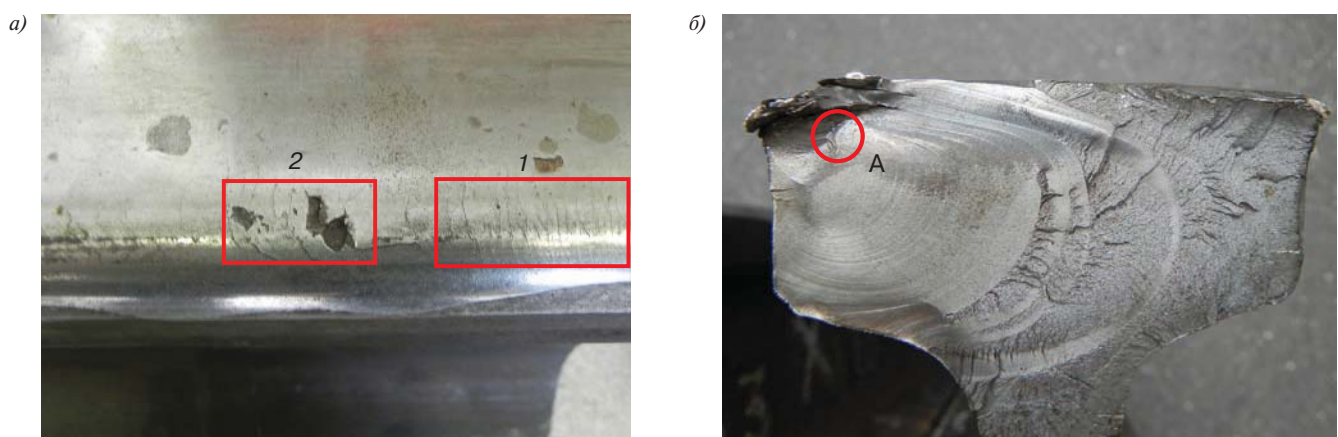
Варианты разрушения в области сварных стыков:
